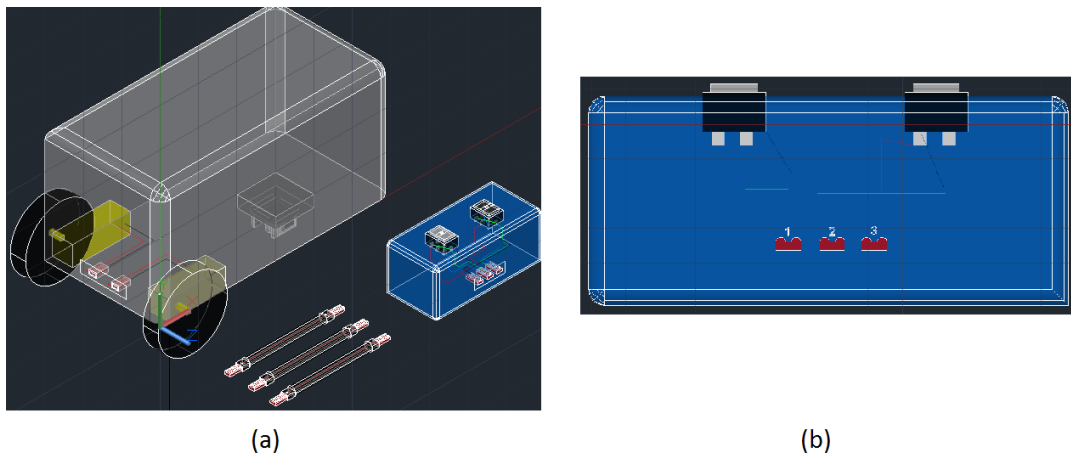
(a) Desenho em 3D do robô, incluindo: chassi, controle e cabos. (b) Detalhe do controle.
